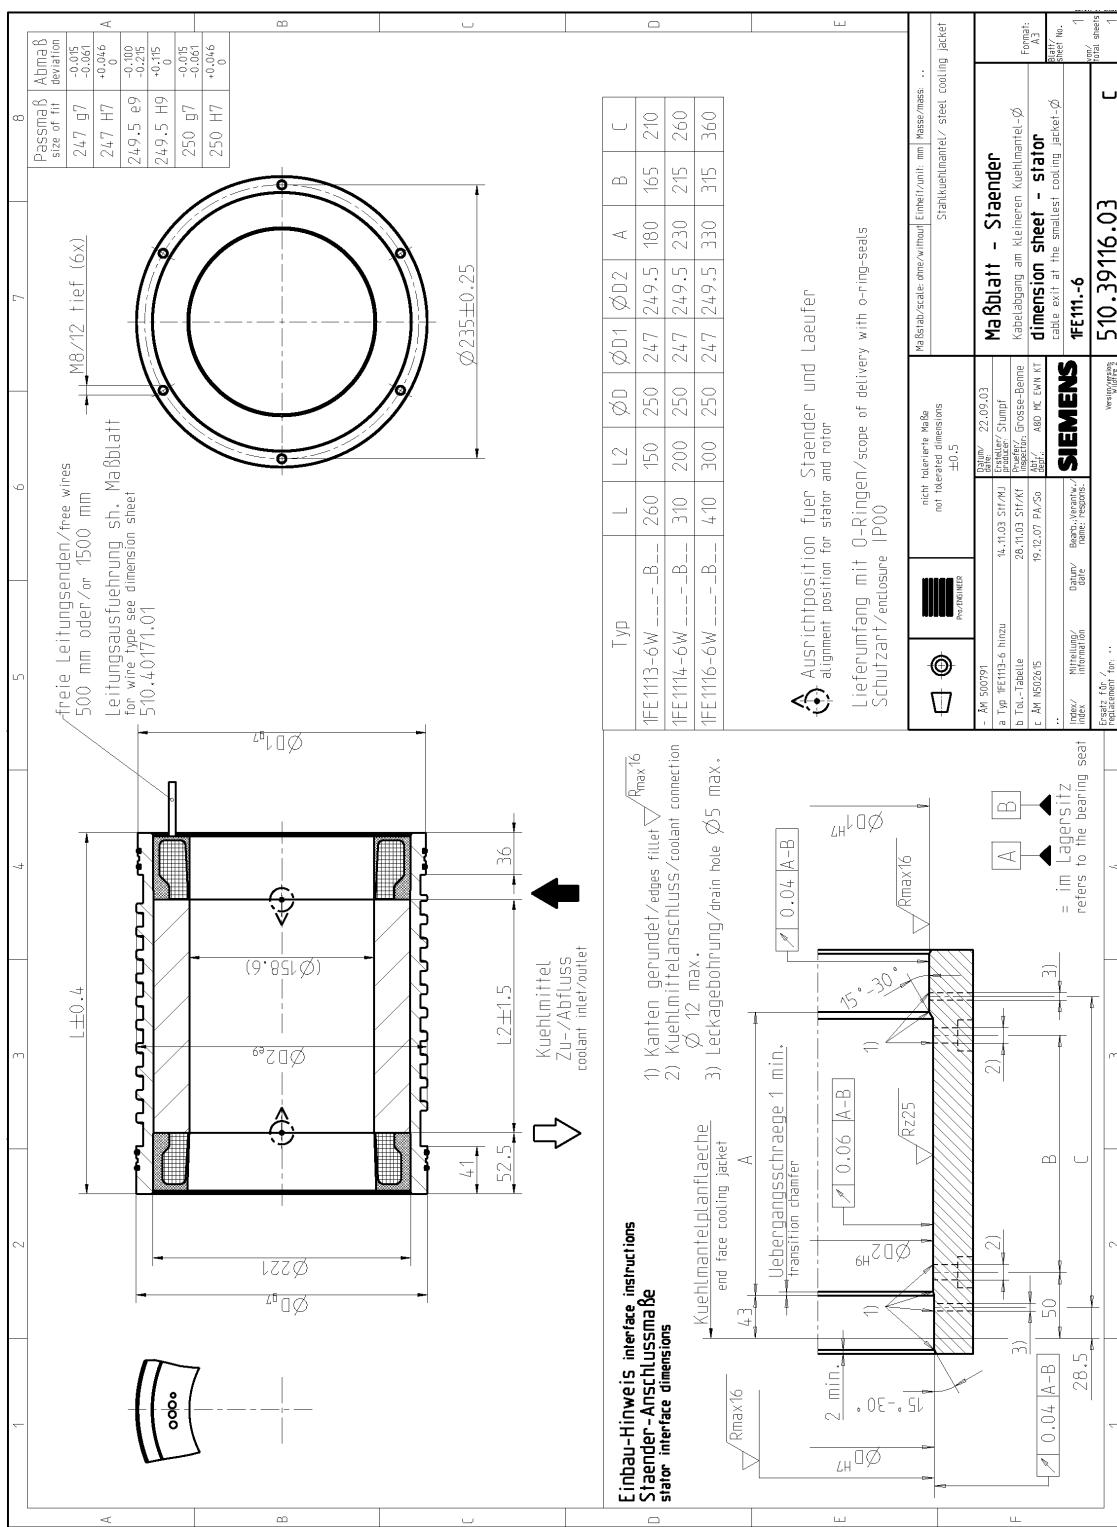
1FE111□-6, Ständer mit Kühlmantel, Kabelabgang am kleineren Kühlmanteldurchmesser
